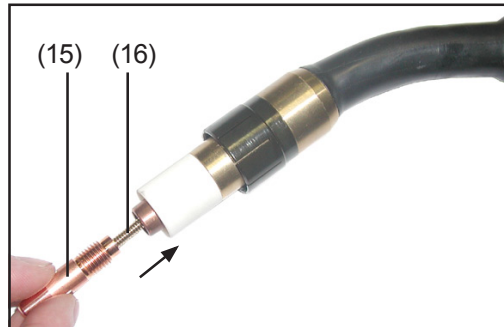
Draht-Führungsseele zurückschieben und Kontaktrohr festschrauben
